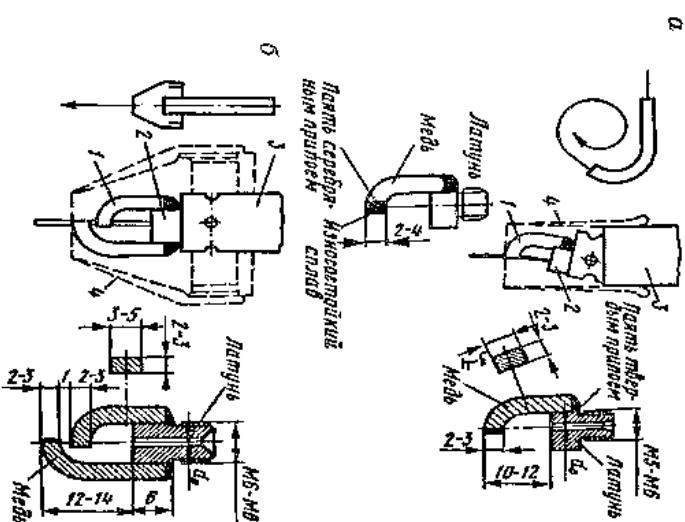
Контакты держателя для изогнутой (а) и прямой (б) мундштуков при сварке проволокой 0,5—1,2 мм:
